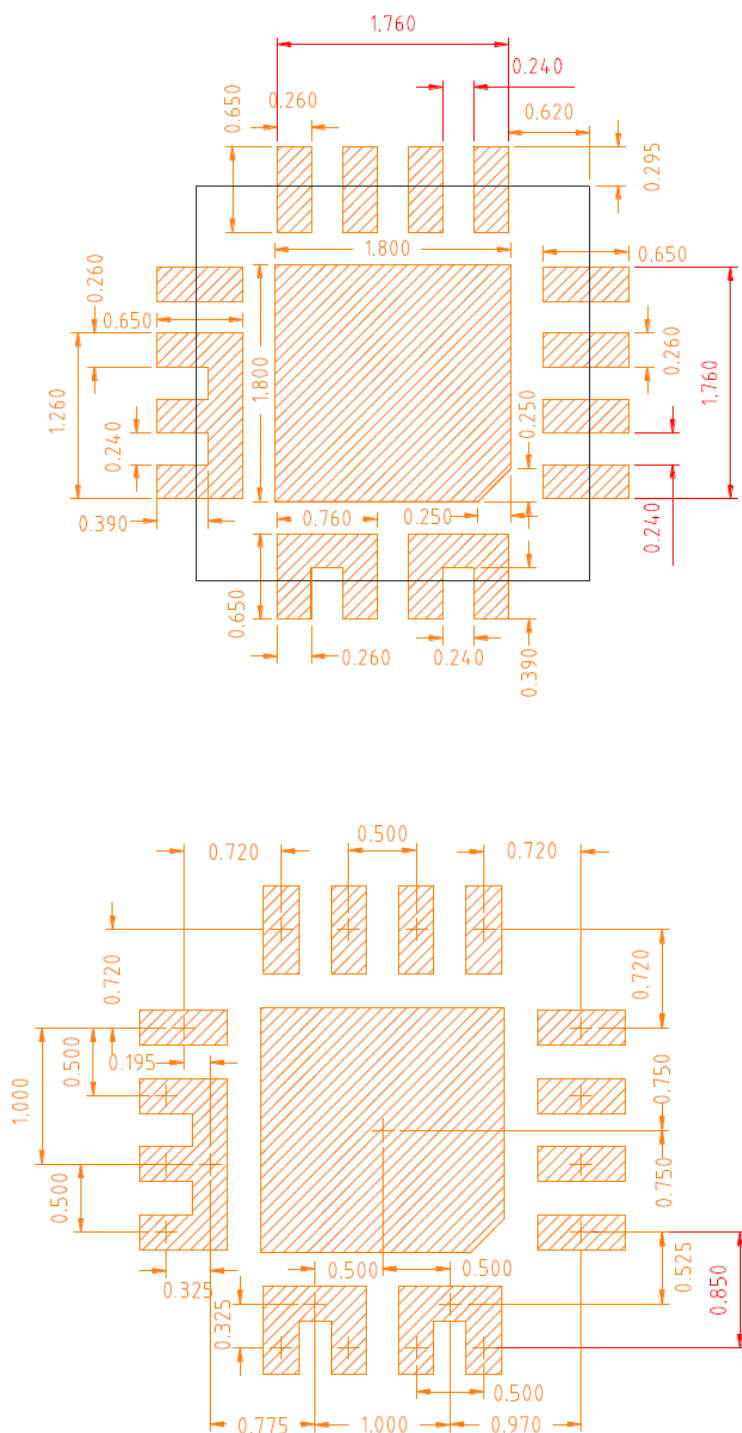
PCB 金属焊盘尺寸和间距 (所有尺寸均以 mm 为单位)
